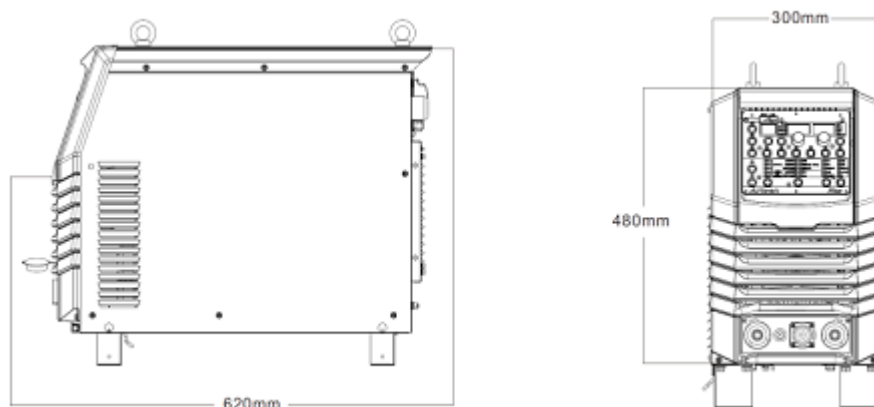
Габаритные размеры источника сварочного тока
